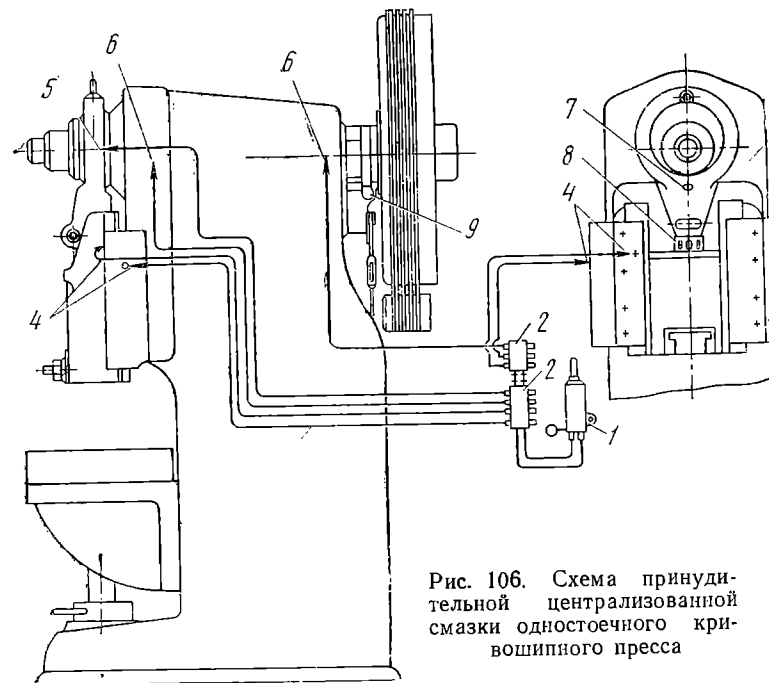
Схема принудительной централизованной смазки одноствоечного кривошипного прессы
